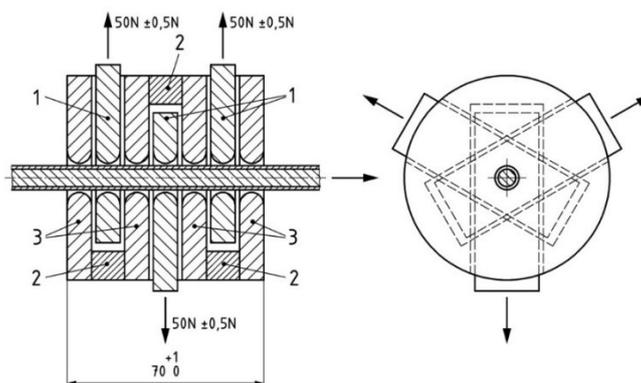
Схема пристрою для вимірювання зміщення обплетення: 1 - рухомі пластини; 2 - проставка; 3 - фіксовані пластини.
